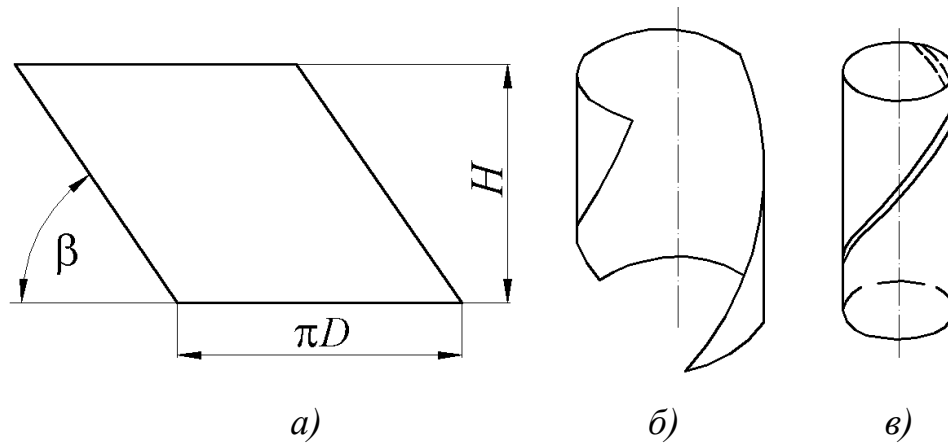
Етапи формування згортої втулки з гвинтовим стиковим швом [8]: а) – заготовка (карточка); б) – часткова згортка втулки; в) – згортна втулка
